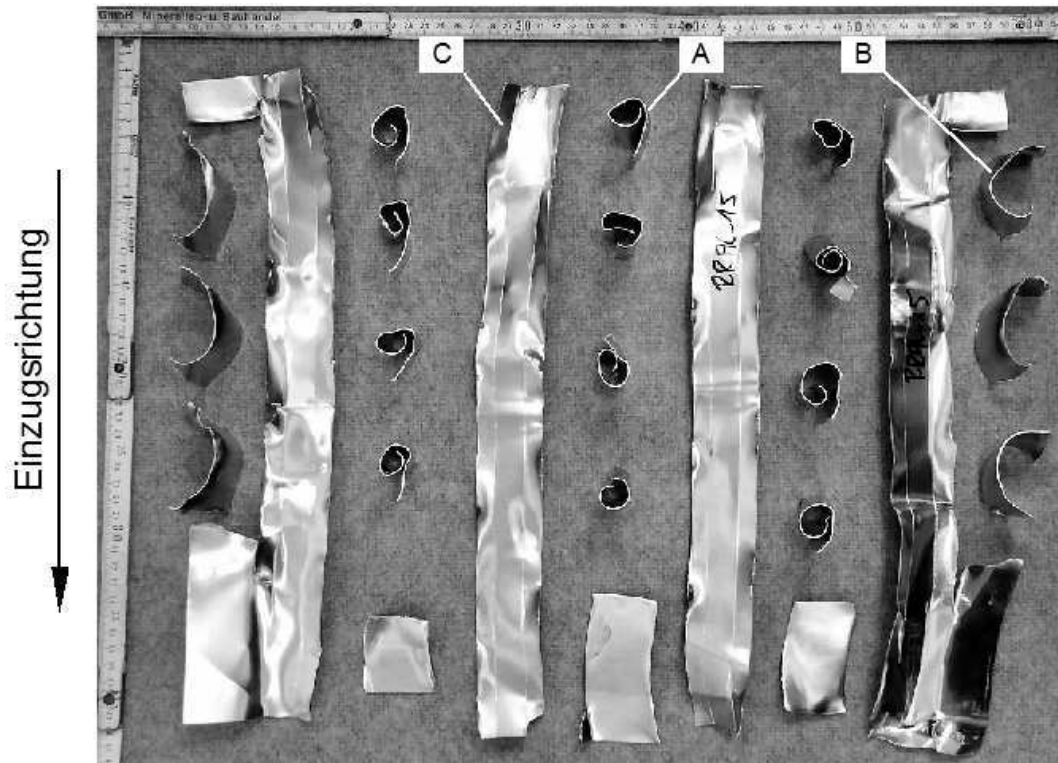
Bruchstücke eines mit dem einrotorigen Rotorreißer zerkleinerten AlMg3-Bleches Wanddicke 1 mm; (A) unterhalb der Rotormesser eingerollte Stücke; (B) Randstücke; (C) unzerkleinerte Reststücke der Statorwerkzeuge
